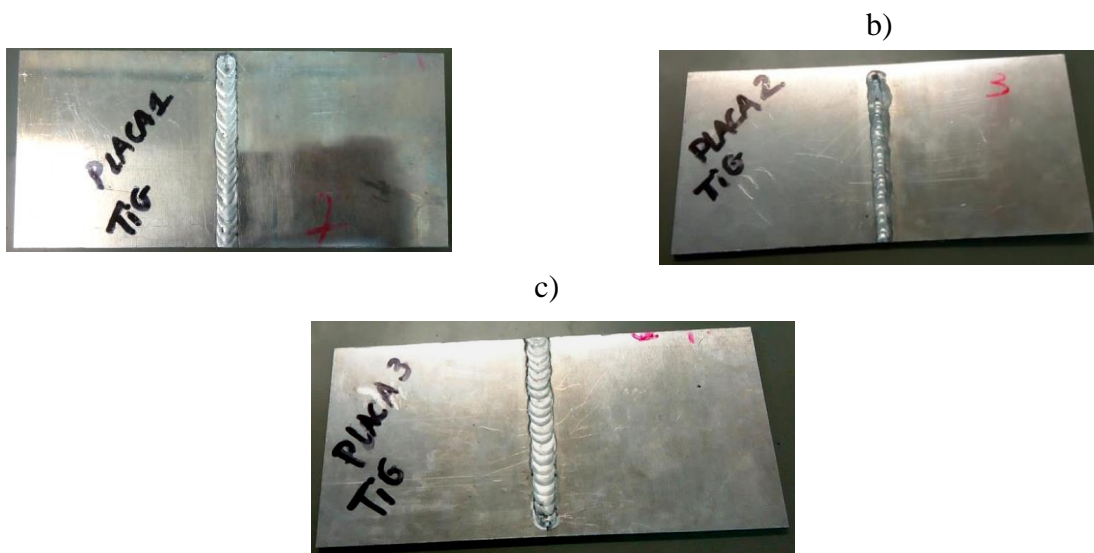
Placas com juntas soldadas por TIG. A) Placa 1; b)Placa 2;c) Placa 3.
